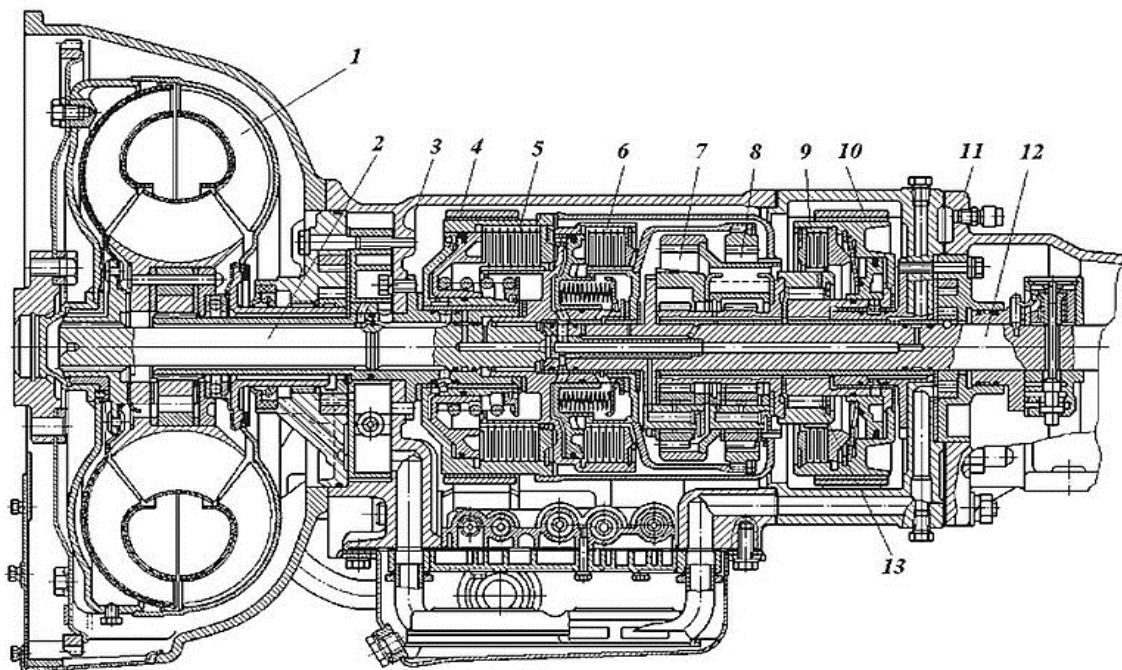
АКП с трехступенчатой планетарной коробкой передач:
